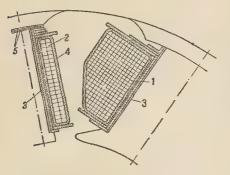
Добавочный и главный полюсы с обмотками.
